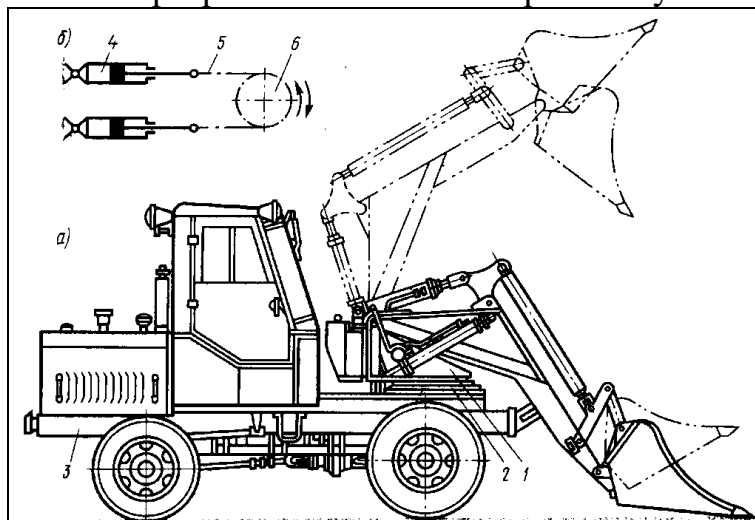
Полуповоротный одноковшовый погрузчик: а — схема конструкции; б — кинематическая схема механизма вращения платформы
